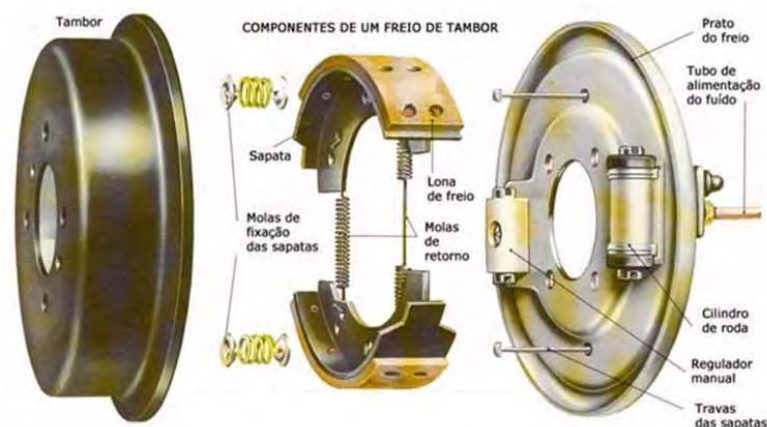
Principais componentes de um freio à tambor. (DPK, 2019)
